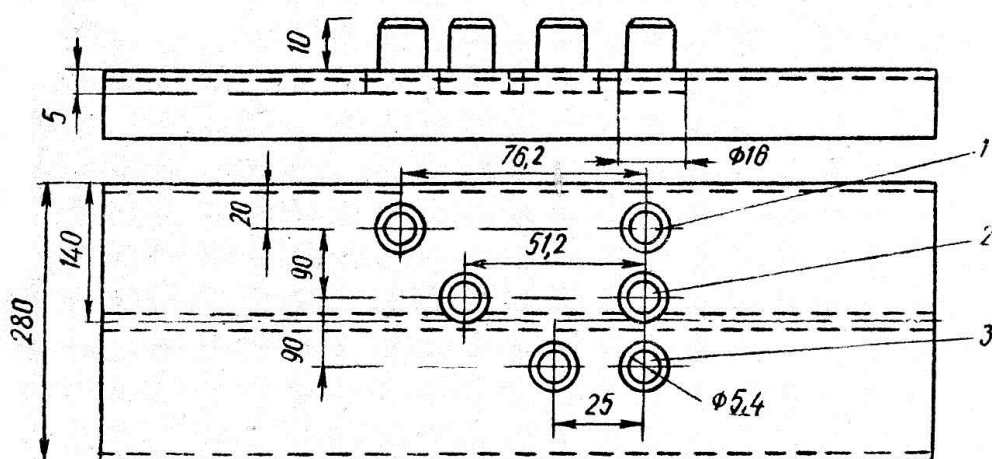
Кондуктор для зварювання спинки ножа різального апарата:
